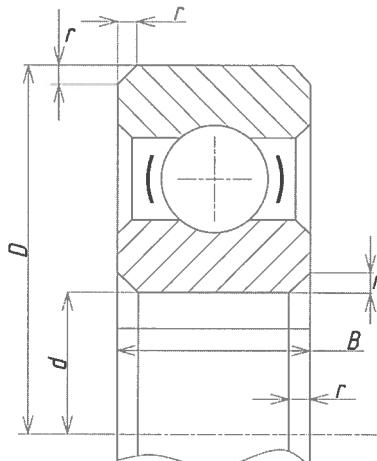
Конструкция подшипника шарикового радиального однорядного
